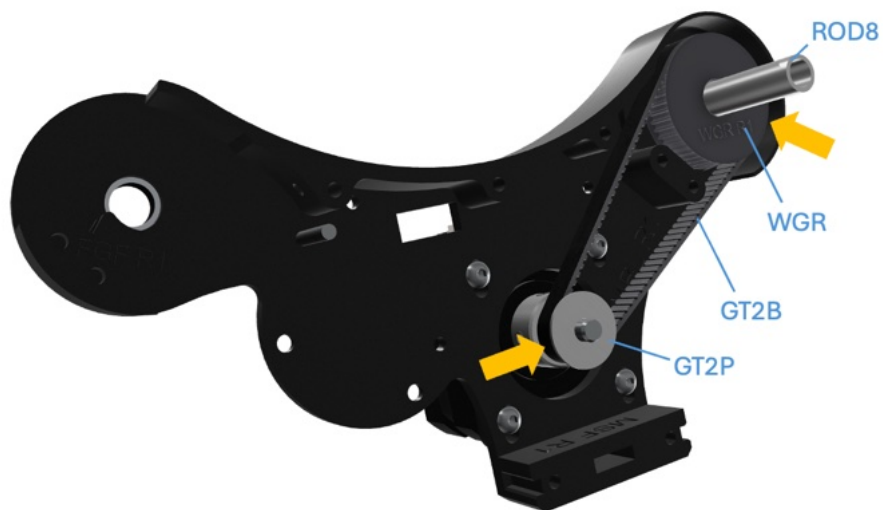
Rewinder-Chassis Montageschritt 9.
